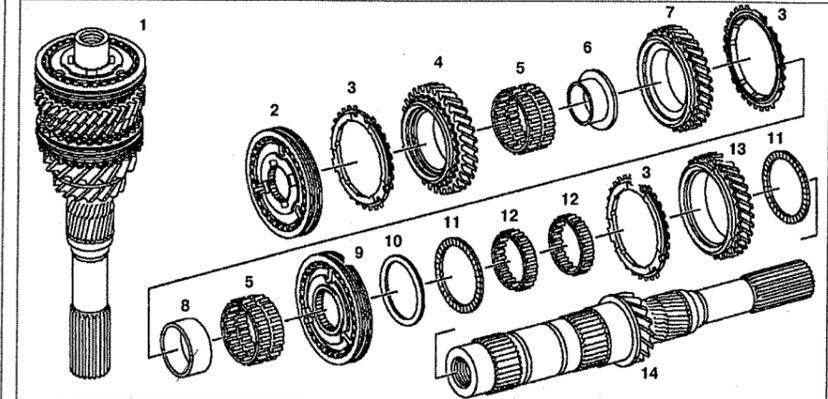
Ведущий вал (автомобили с двигателем 611.980):
